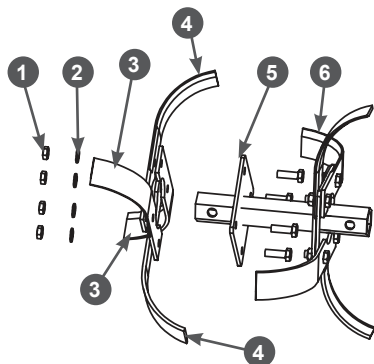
Установка ножей на внешний фланец основной секции оси фрезы
